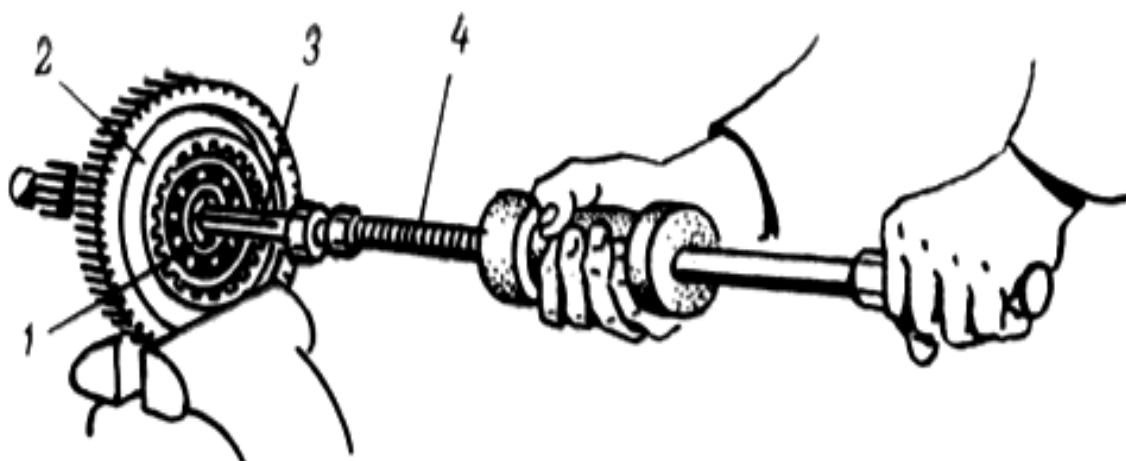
Випресування підшипника з вторинного вала: 1- підшипник; 2- вторинний вал; 3- цанга; 4- інерційний знімач
